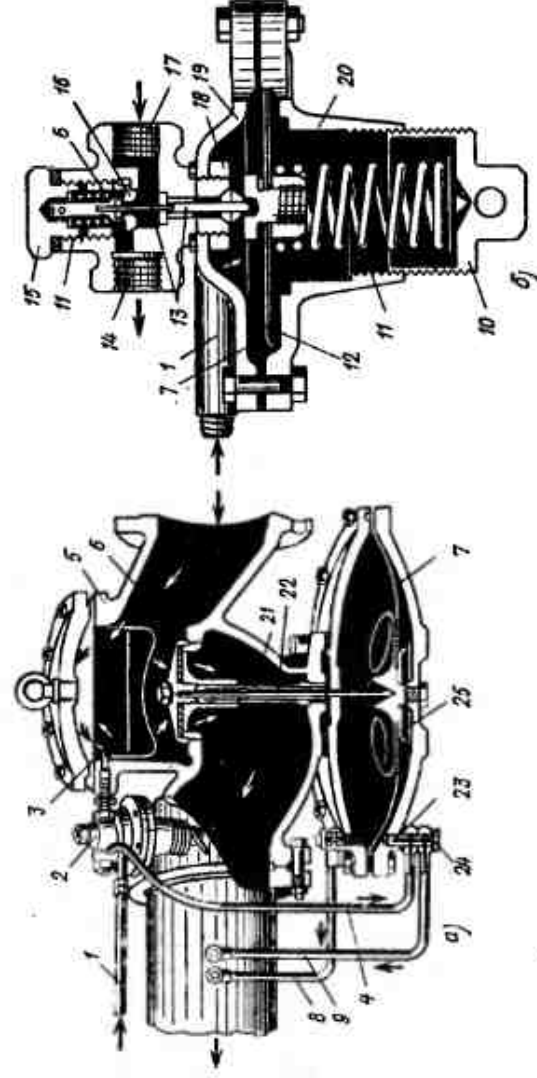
Устройство и схема обвязки регулятора РДУК-2:
